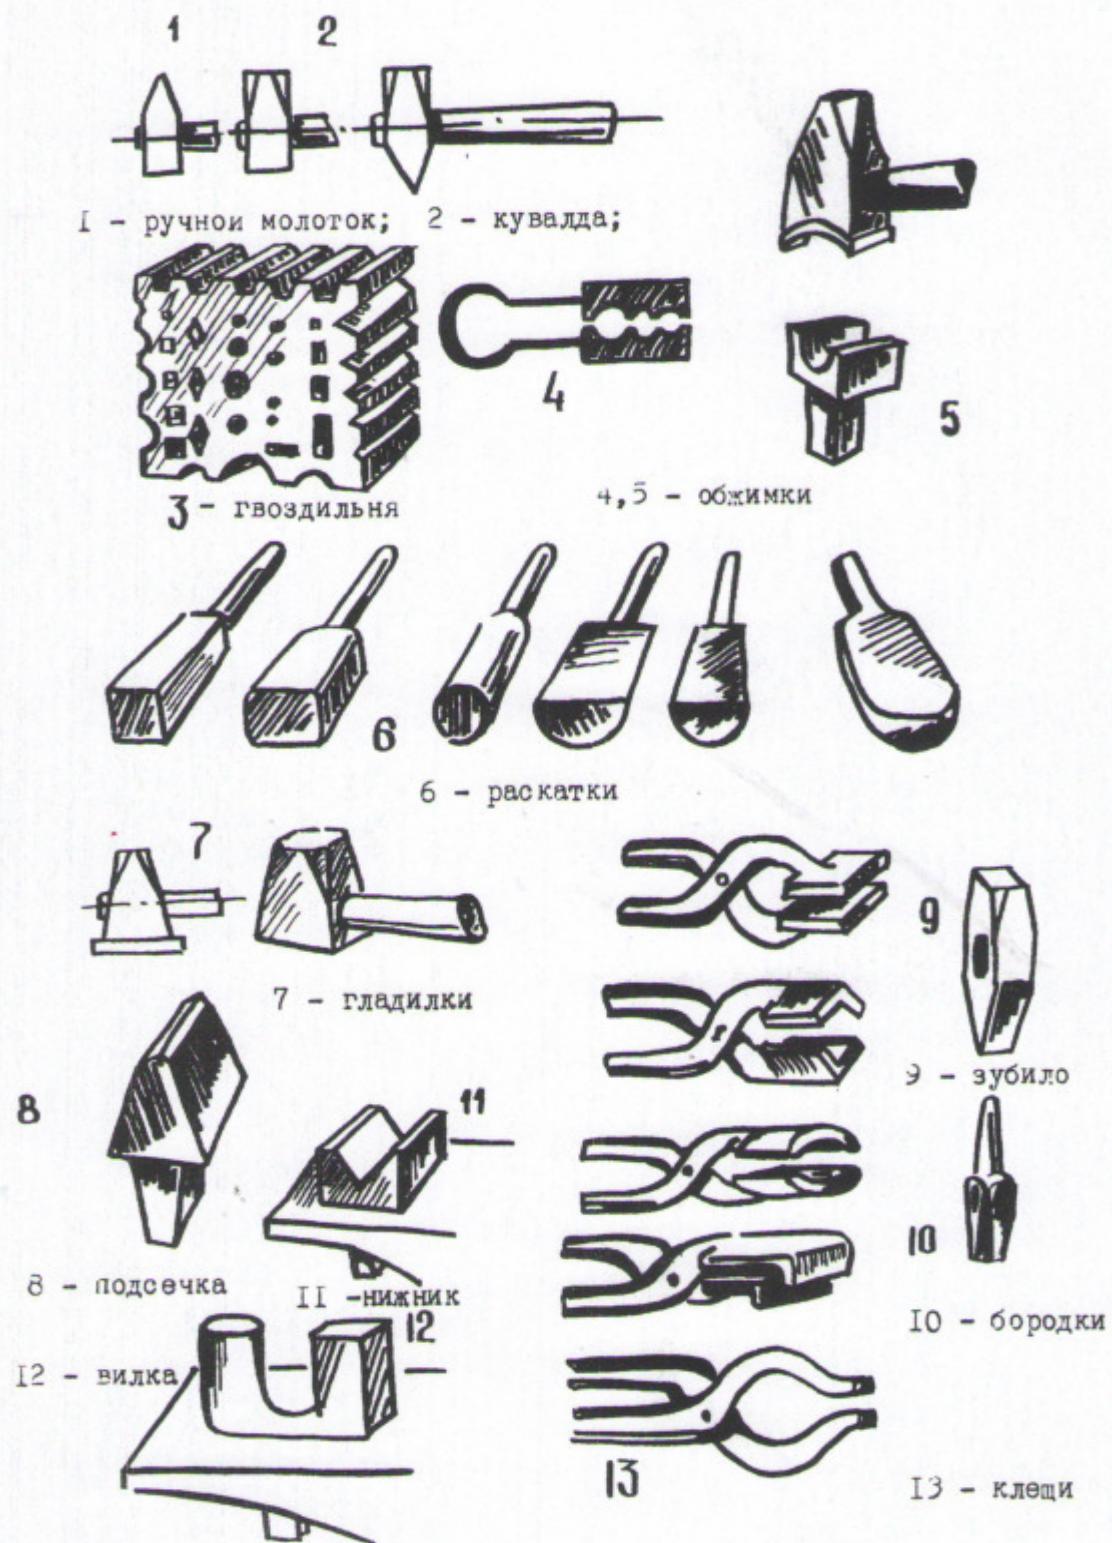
Инструменты и приспособления для свободной ручной ковки для всевозможных гибочных работ, а также для изготовления особо мелких поковок
